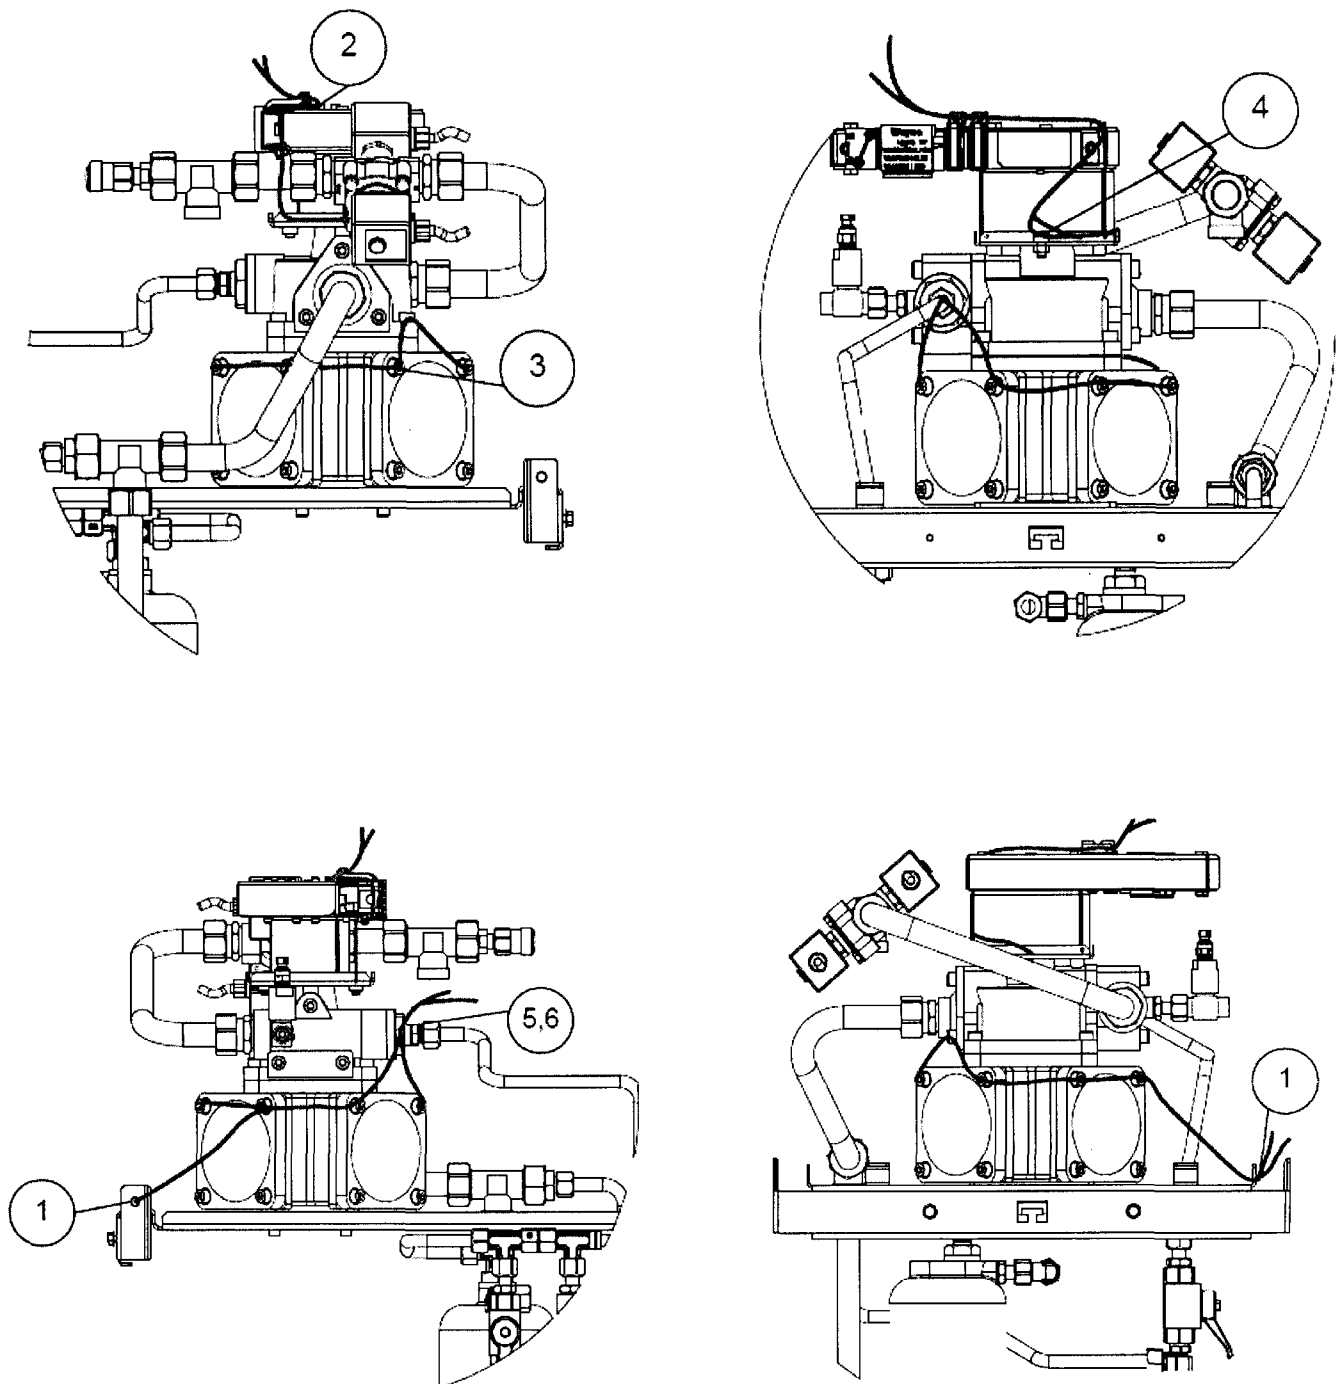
Схема нанесения знака поверки на LPG6000
